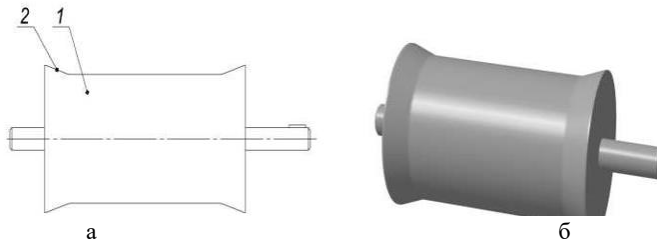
Барабан ленточного конвейера: а) 2D вид; б) 3D вид; 1 – центральный цилиндрический участок; 2 – торцевой конический участок
